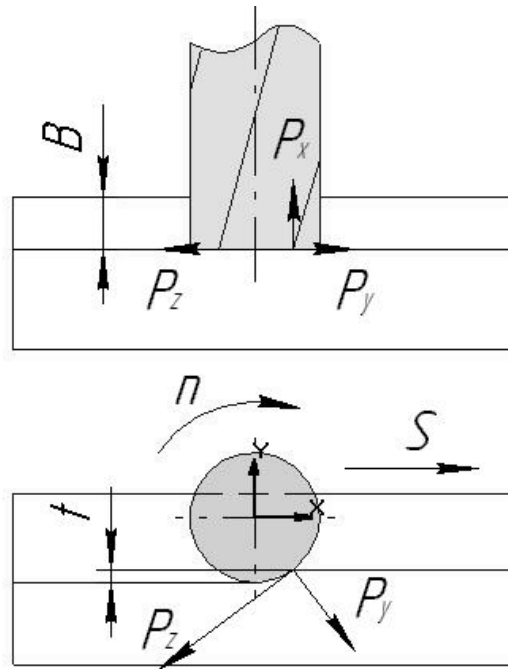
Схема фрезерування та розташування сил різання
